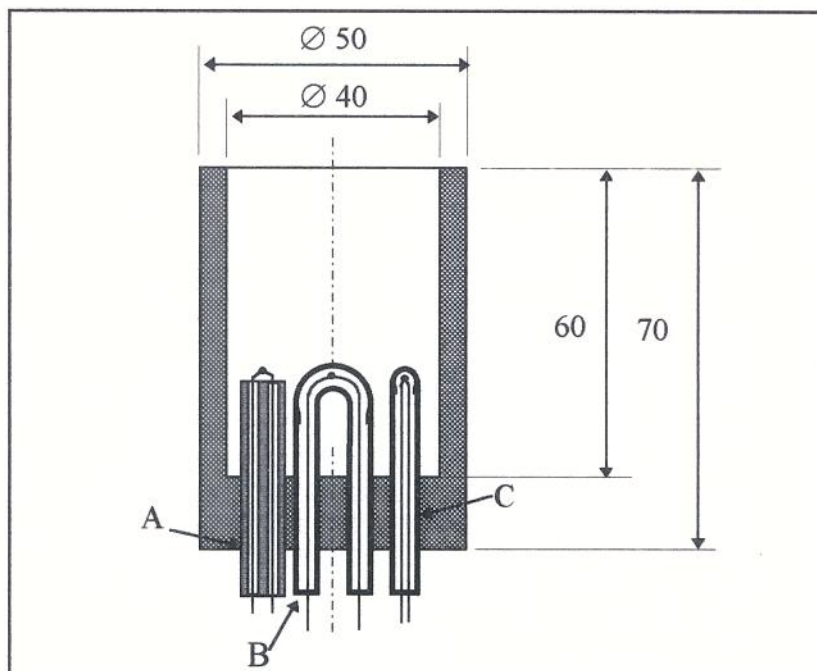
Desenho esquemático da montagem dos termopares no molde utilizado
